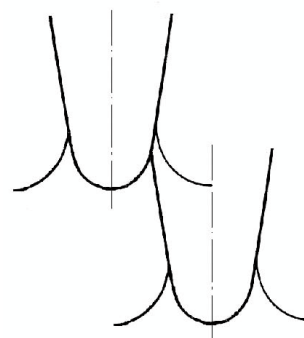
Схема почвообрабатывающей саморазвёртывающейся скобы
